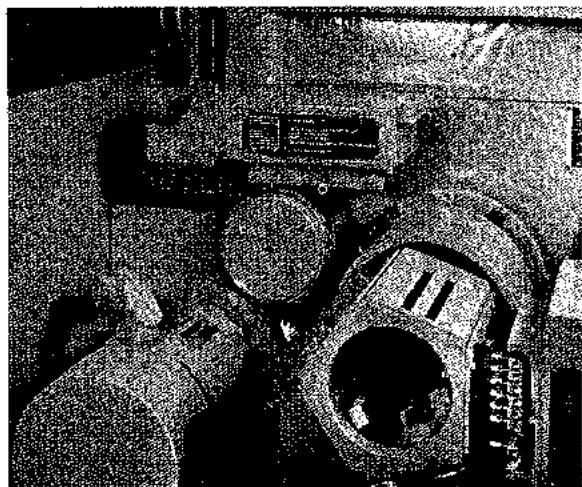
Conjunto del tambor de levas y tambor de mando principal de una máquina de mandril automático y de un solo husillo (Warner & Swasey Co.)
